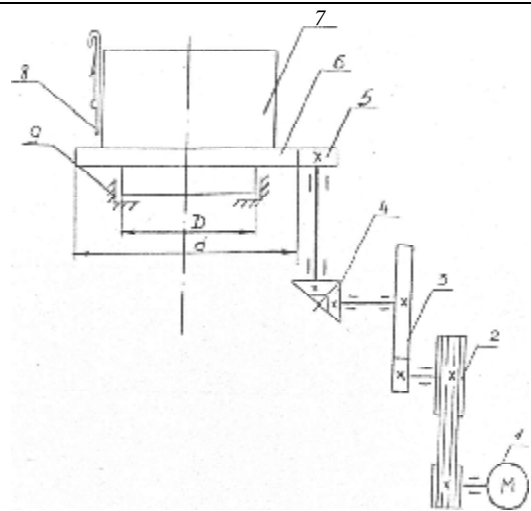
Кінематична схема приводу голкового циліндра круглов'язальної машини: 1 – електродвигун; 2 – клинопасова передача; 3 – циліндрична зубчаста передача; 4 – конічна зубчаста передача; 5 – циліндрична зубчаста шестерня; 6 – циліндричне зубчасте колесо; 7 – голковий циліндр; 8 – голки; 9 – опора
